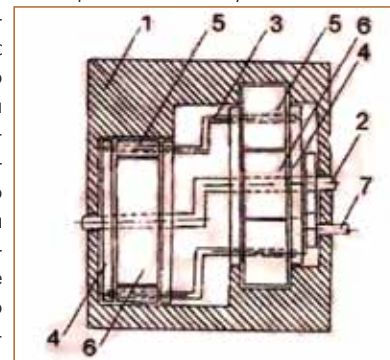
Схема диско-лопастной спарки: 1 - корпус, 2 - коленчатая ось (не вращающаяся), 3 - коленчатый вал, 4 - диск, 5 - лопасть, 6 - внутренний корпус, 7 - выходной вал.
